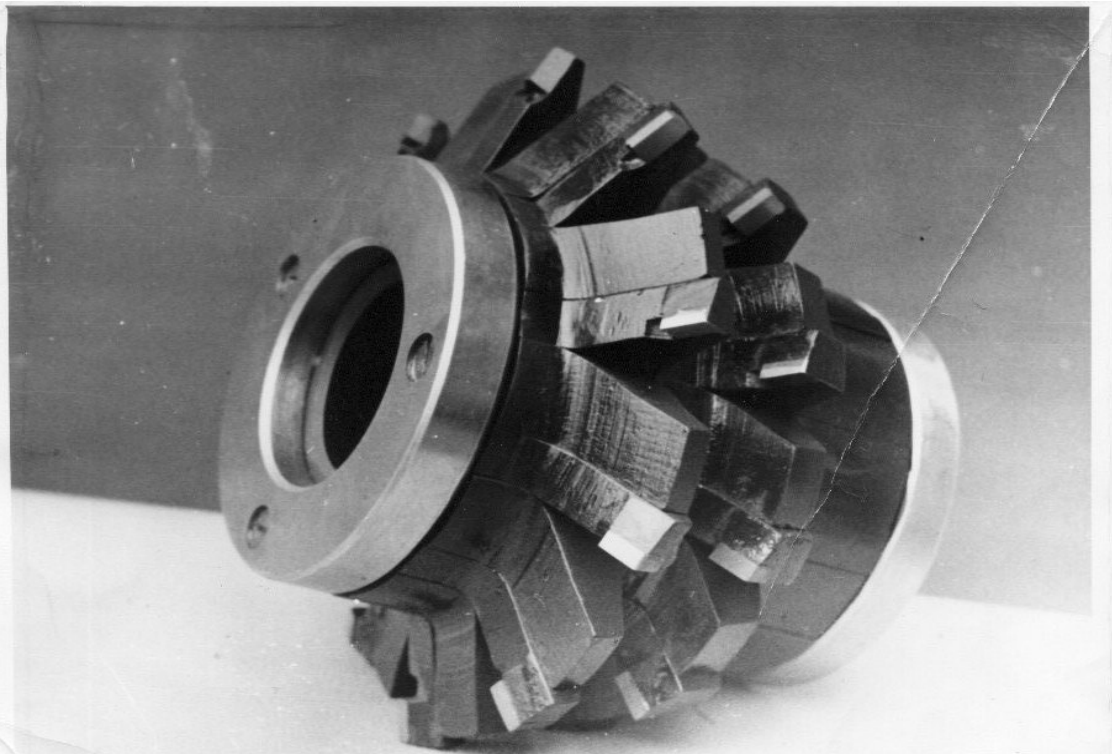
Правый корпус червячной фрезы  $m=16$  мм со вставными рейками и напаянными твердосплавными пластинами.
